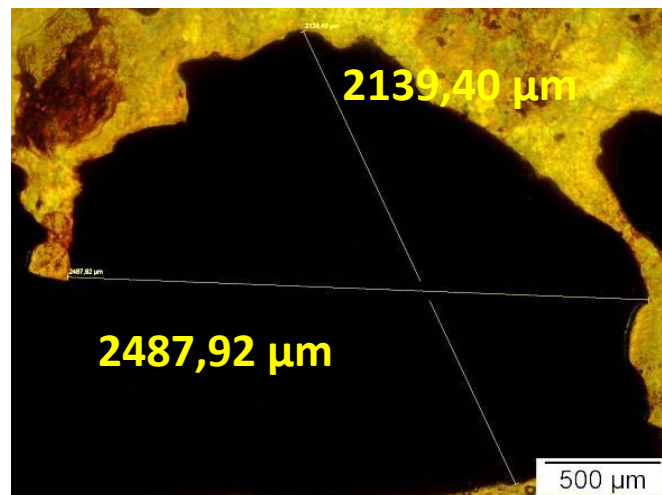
Imagens microscópicas da chapa soldada com vento mostrando trinca e falta de fusão, localizados entre o MB e o cordão de solda.
